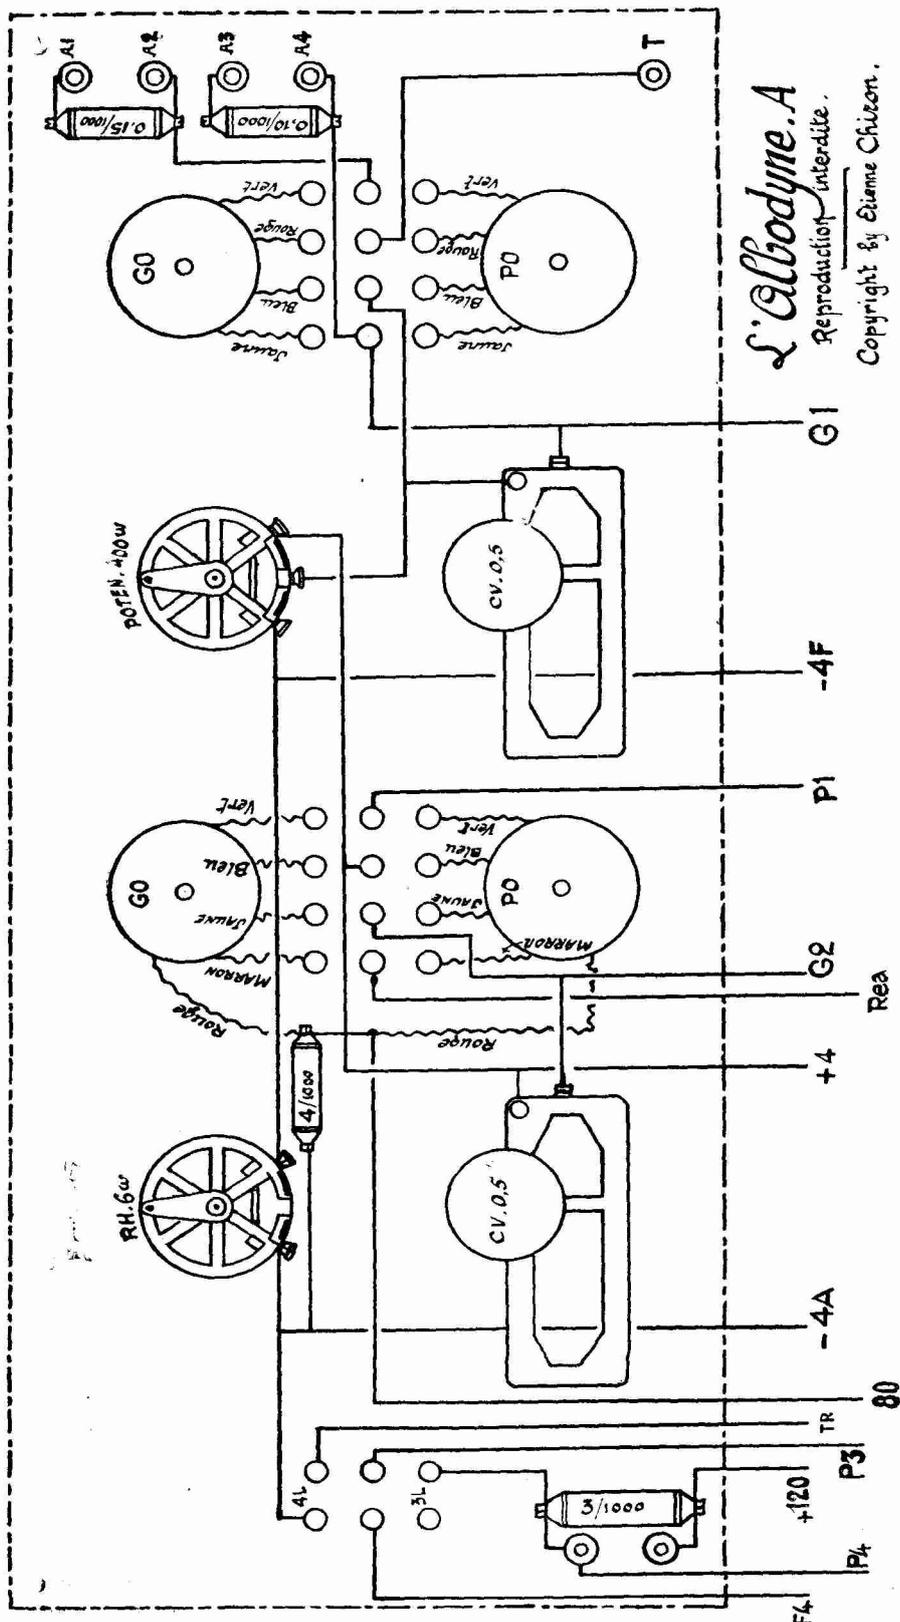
Plan du câblage du panneau frontal (réduction du plan grandeur naturelle).
